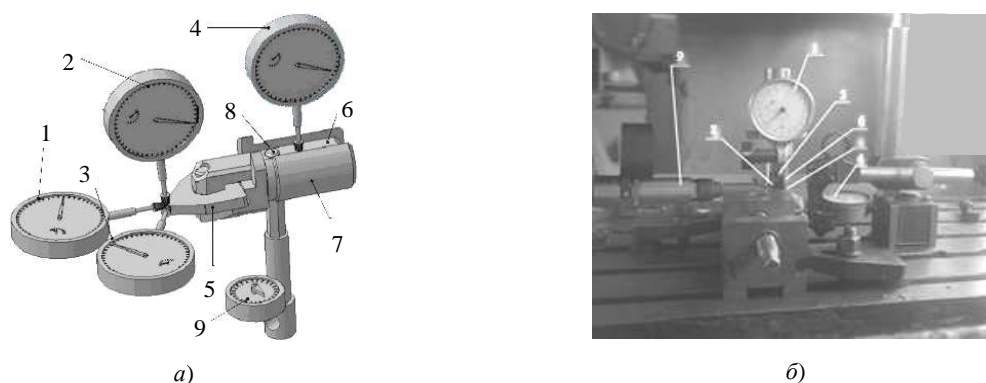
3D-модель (а) и экспериментальная установка (б) для измерения перемещений пластины режущей и прихвата: 1, 2, 3, 4 – индикаторы часового типа; 5 – пластина режущая; 6 – прихват; 7 – блок резцовый; 8 – винт зажимной; 9 – динамометрический ключ
